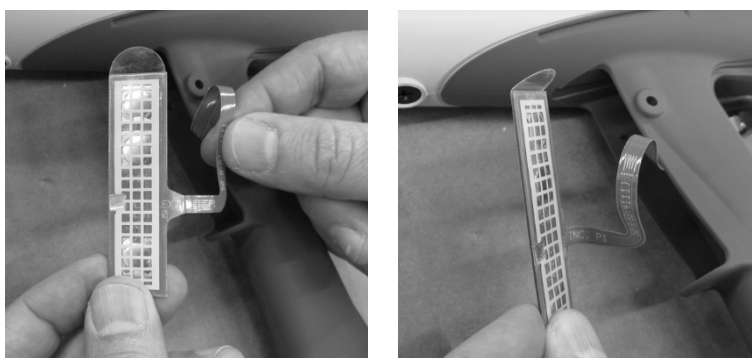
Installazione di un interruttore a grilletto - Passaggio 3
